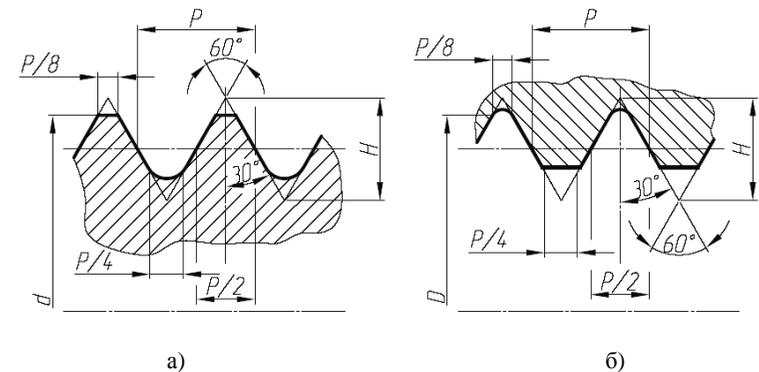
Профиль наружной на валу (а) и внутренней в отверстии (б) метрической цилиндрической резьбы
